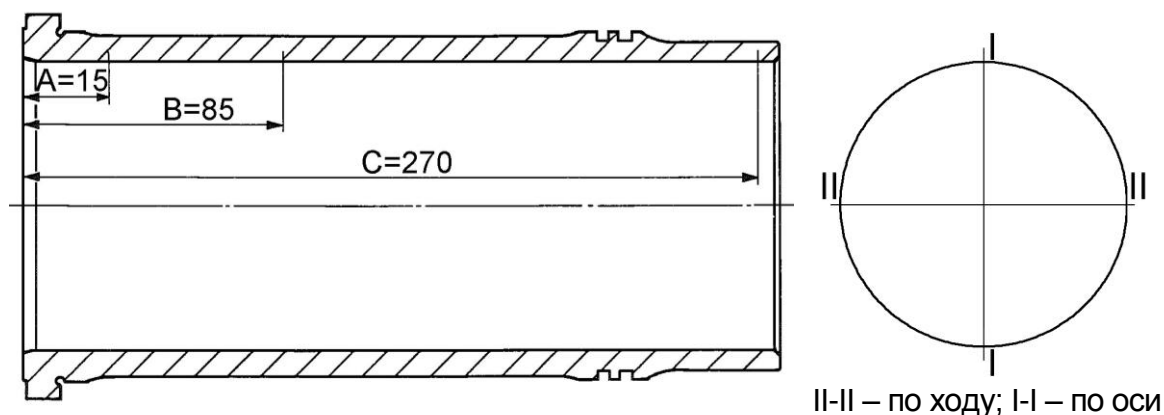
Схема обмеров втулки цилиндра дизелей типа 3Д6 и 7Д12
